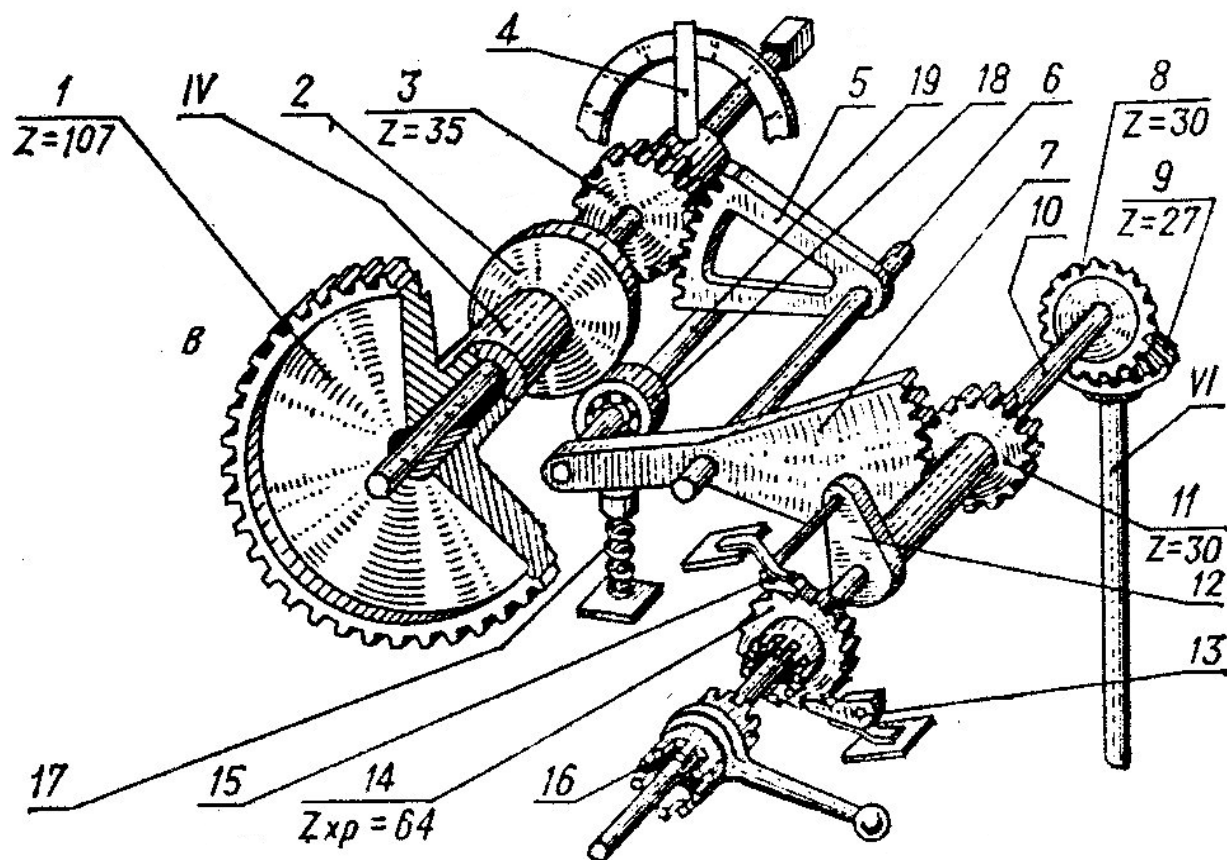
Механизм поперечной подачи: 1 – колесо кулисное; 2 – кулачок; 3, 11 – колесо зубчатое цилиндрическое; 4 – указатель величины подачи; 5, 7 – сектор зубчатый; 6 – валик; 8, 9 – колесо коническое зубчатое; 10 – валик; 12 – поводок; 13, 15 – собачка; 14 – колесо храповое; 16 – муфта кулачковая; 17 – пружина
